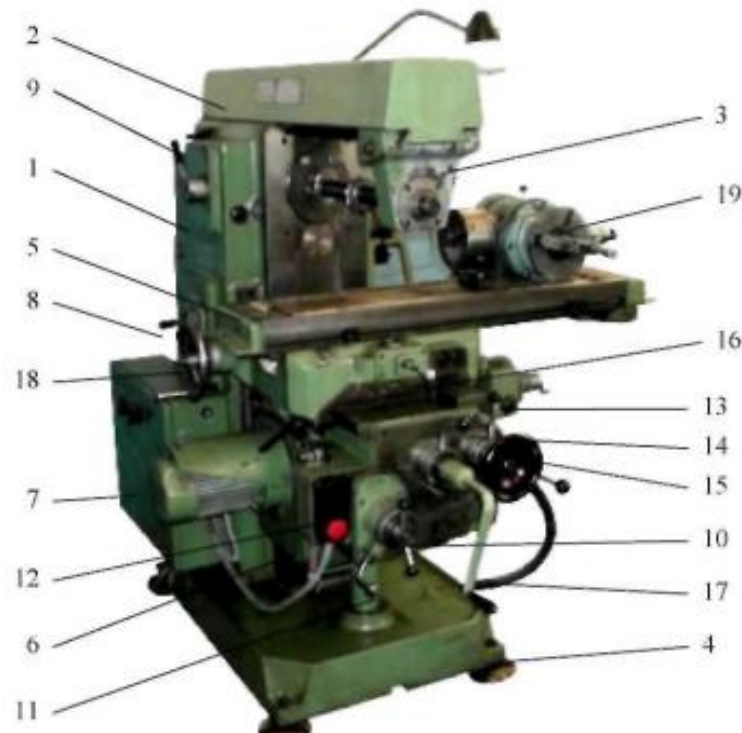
Общий вид универсально-фрезерного станка модели 6P811; 1 - станина с коробкой скоростей и шпиндельным узлом; 2 - хобот; 3 -серьга; 4 - основание; 5 - стол; 6 - консоль с коробкой подач; 7 - электрошкаф 8 -рукоятка переключения перебора коробки скоростей; 9 - рукоятка переключения частот вращения шпинделя; 10 - рукоятка переключения величин подач стола; 11 -рукоятка переключения перебора коробки подач; 12 - кнопки управления электродвигателями; 13 -рукоятка включения механической поперечной подачи стола; 14 -рукоятка включения механической вертикальной подачи консоли; 15 - маховичек ручного поперечного перемещения стола; 16 -рукоятка включения механической продольной подачи стола; 17 - рукоятка ручного вертикального перемещения консоли; 18 - маховичек ручного продольного перемещения стола; 19 - лимбовая делительная головка
